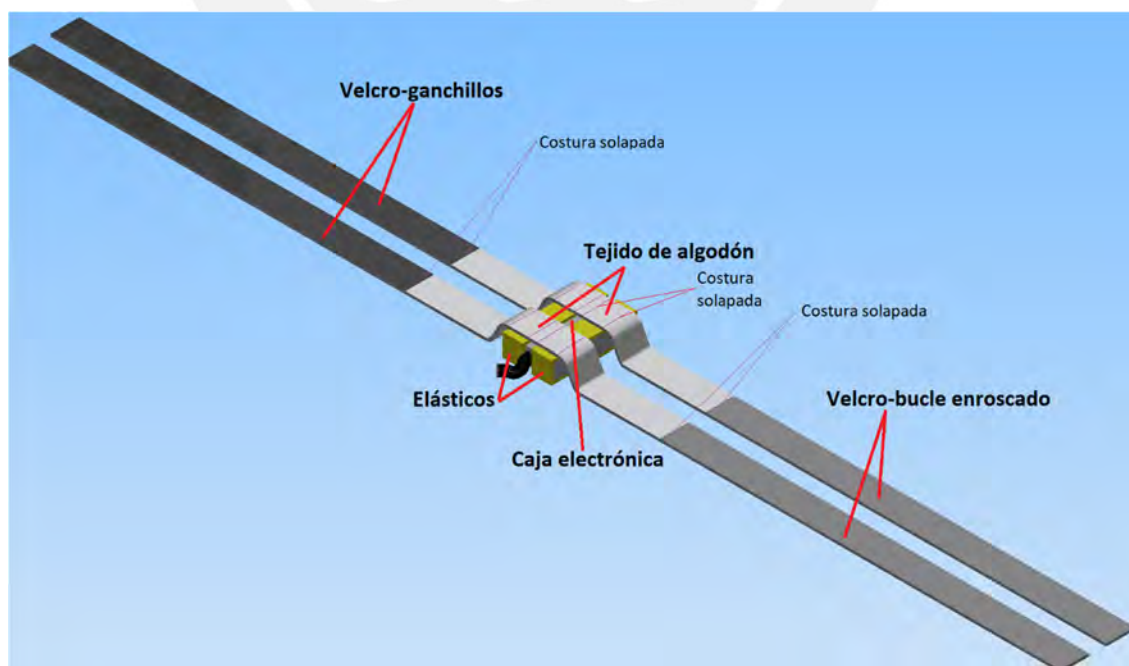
Sujetador del sensor ajustando la caja del sensor
